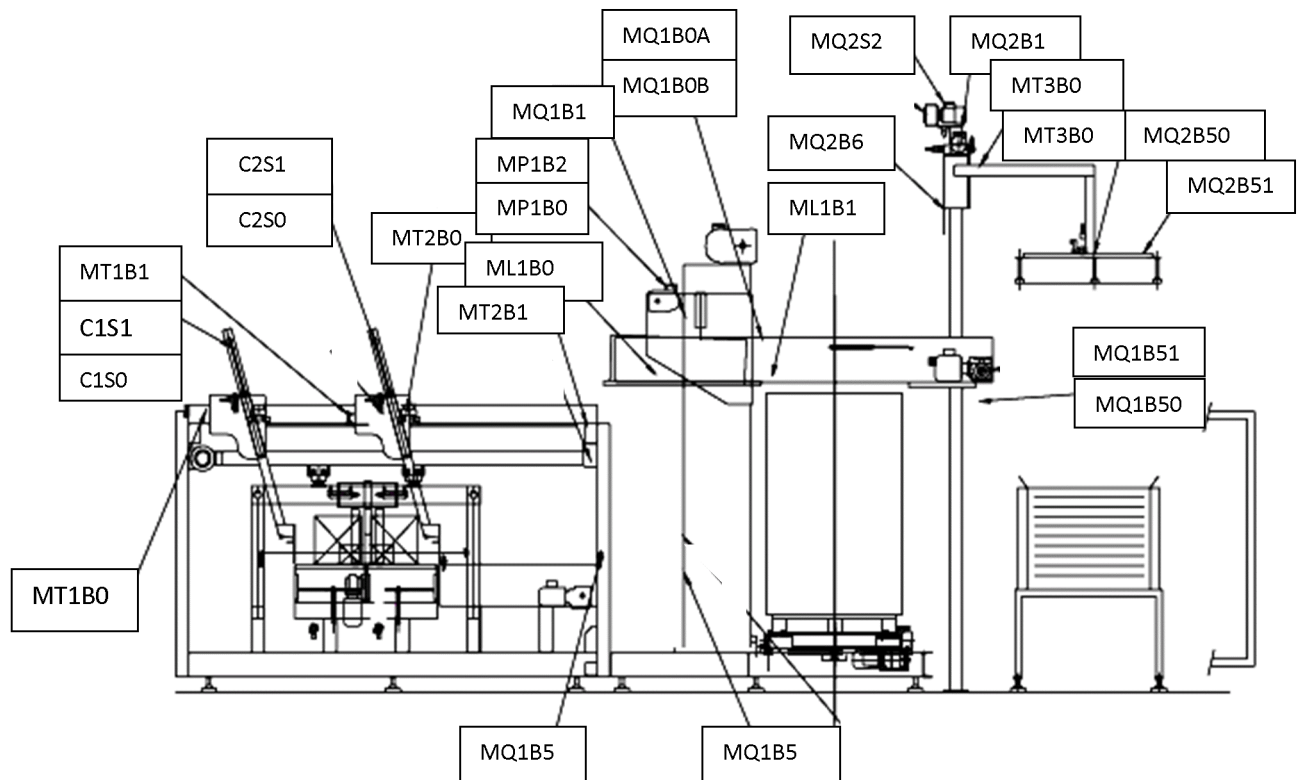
b : Implantation des capteurs vue de face sur la machine palettiseur.
